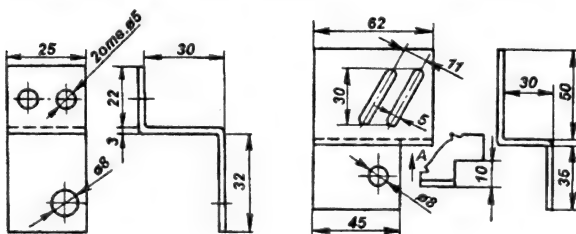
Кронштейн крепления пластины генератора под левую лапку ручного стартера
